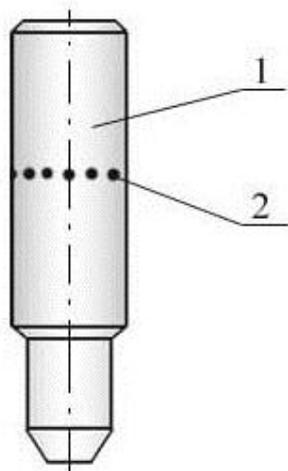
Химическая торпеда-труборезка: 1 – корпус; 2 – струйная насадка
